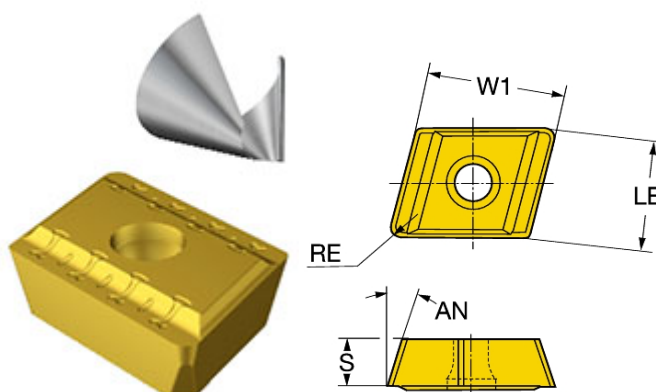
режущая пластина 800-05 03 08M-C-L 1025
